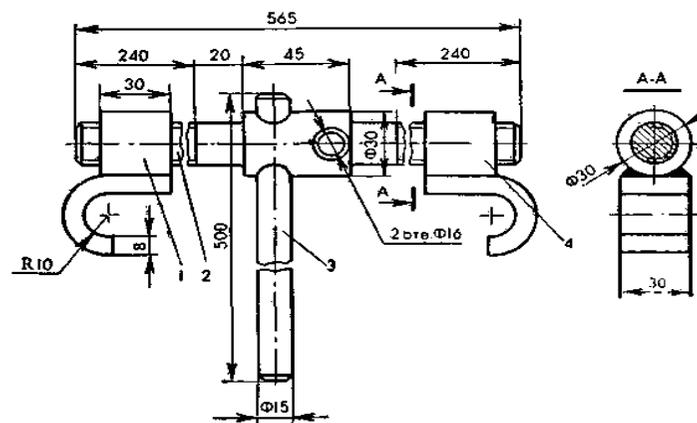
Механическое приспособление для натяжения тяговых цепей: 1, 4 – гайки с зацепом; 2 – винт; 3 – вороток
